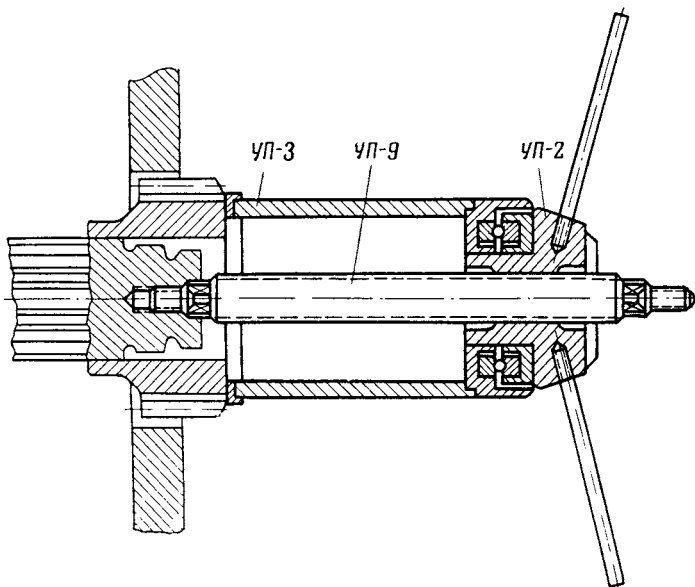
Универсальное приспособление 4800-1-074УП, напресовка шестерен дет. 233-12-144 на промежуточный вал
